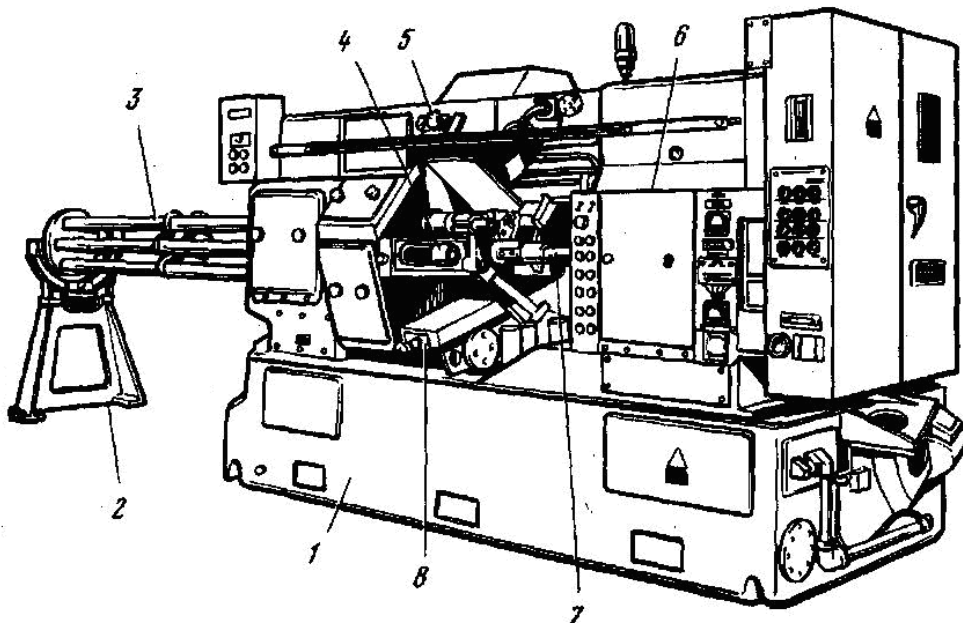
Загальний вигляд шестишпindelного токарного автомата
